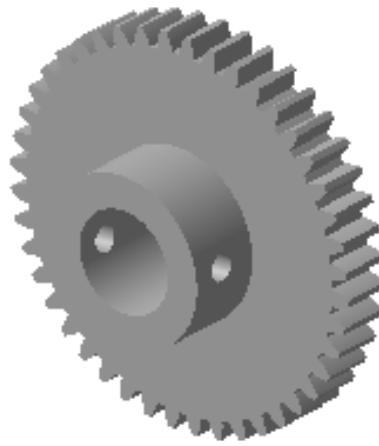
Штифтовий отвір на маточині зубчатого колеса
